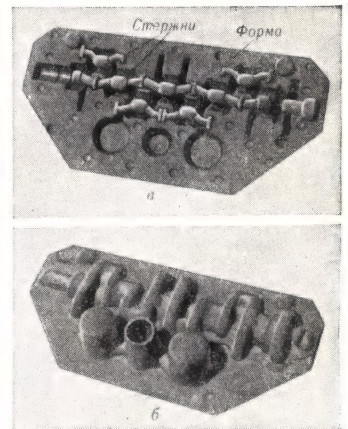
Оболочковая форма для отливки коленчатого вала автомобиля: а — нижняя полуформа с установленными стержнями; б — собранная под заливку форма.
